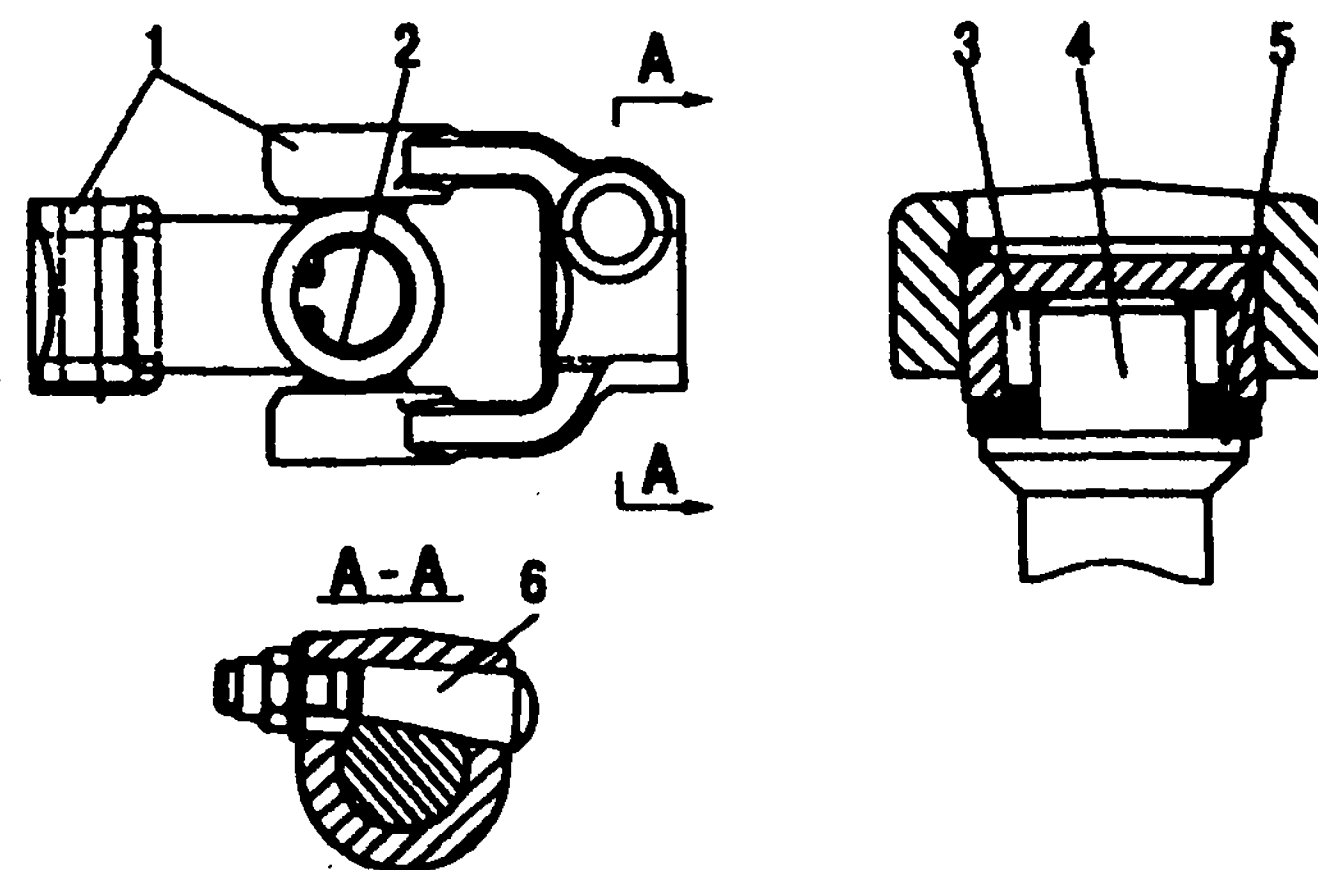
Карданный шарнир: 1 - вилка; 2 - стопорное кольцо; 3 - игольчатый подшипник; 4 - крестовина; 5 - сальник; 6 - клин
